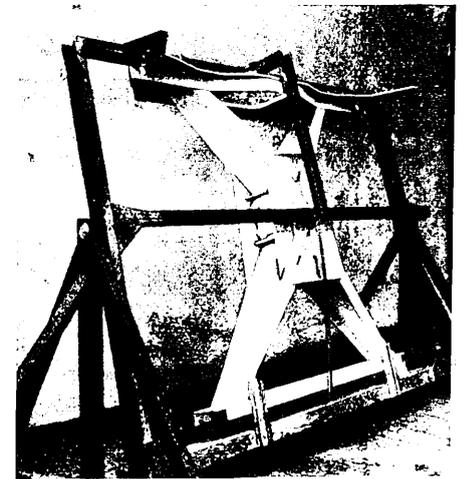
Kopfträger des Großgüterwagens mit anschließendem Diagonalkreuz zur Aufnahme der Zug- und Stoßkräfte in der Schweißvorrichtung.
